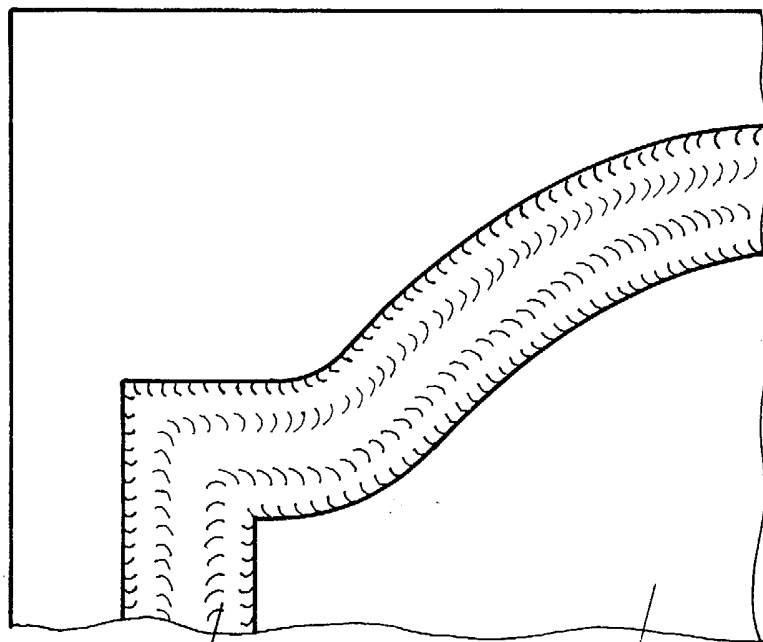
den Abschnitt eines Möbelfront-Bauteiles mit dekorativer Einfräsung in der Draufsicht;
